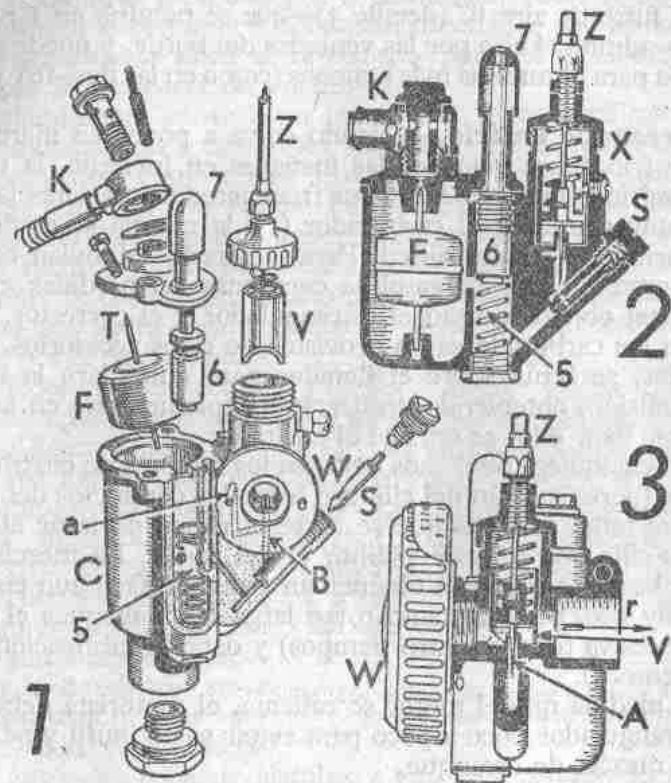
Carburador Dell'Orto para micromotores (hasta 60 cc.).
